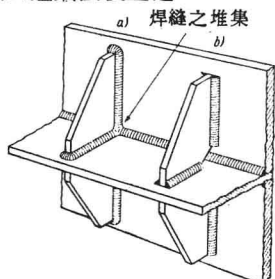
焊接之加強肋條 a) 因焊縫堆集於一處，顯屬不良，b) 焊法正確。
